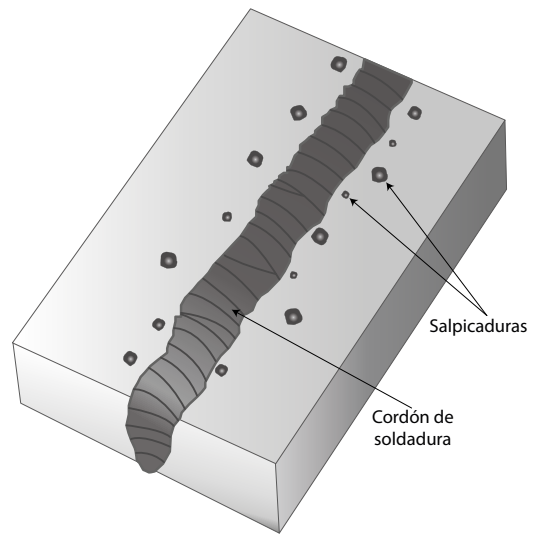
Representación de las salpicaduras y el cordón después de la soldadura
